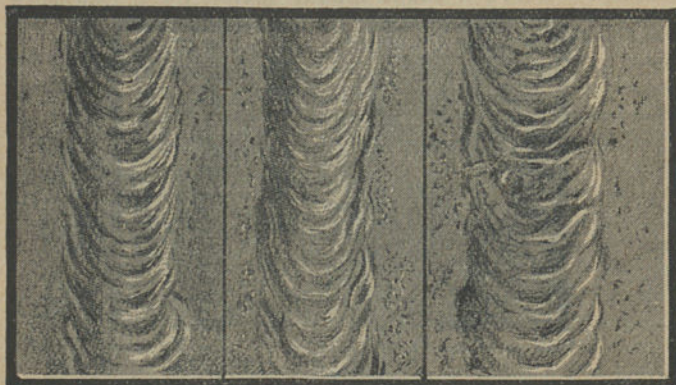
Aspecto de soldaduras de chapa de aço macio de 5 m/m.
